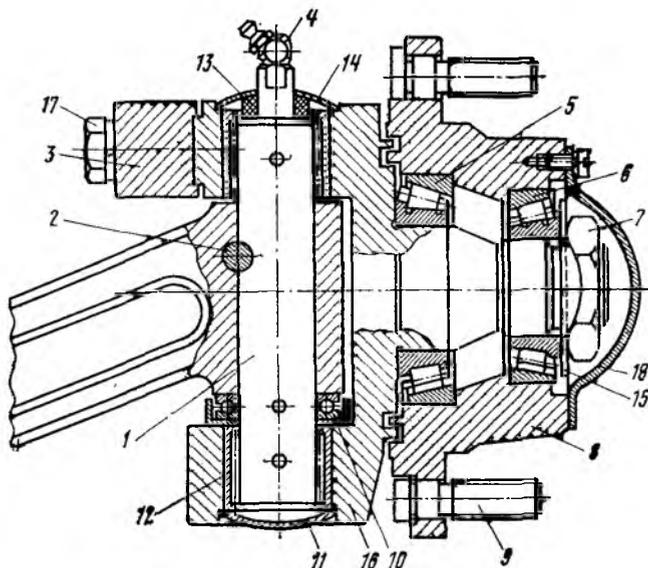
Установка поворотного кулака со ступицей погрузчика Ф7.ЕУ30.32:
